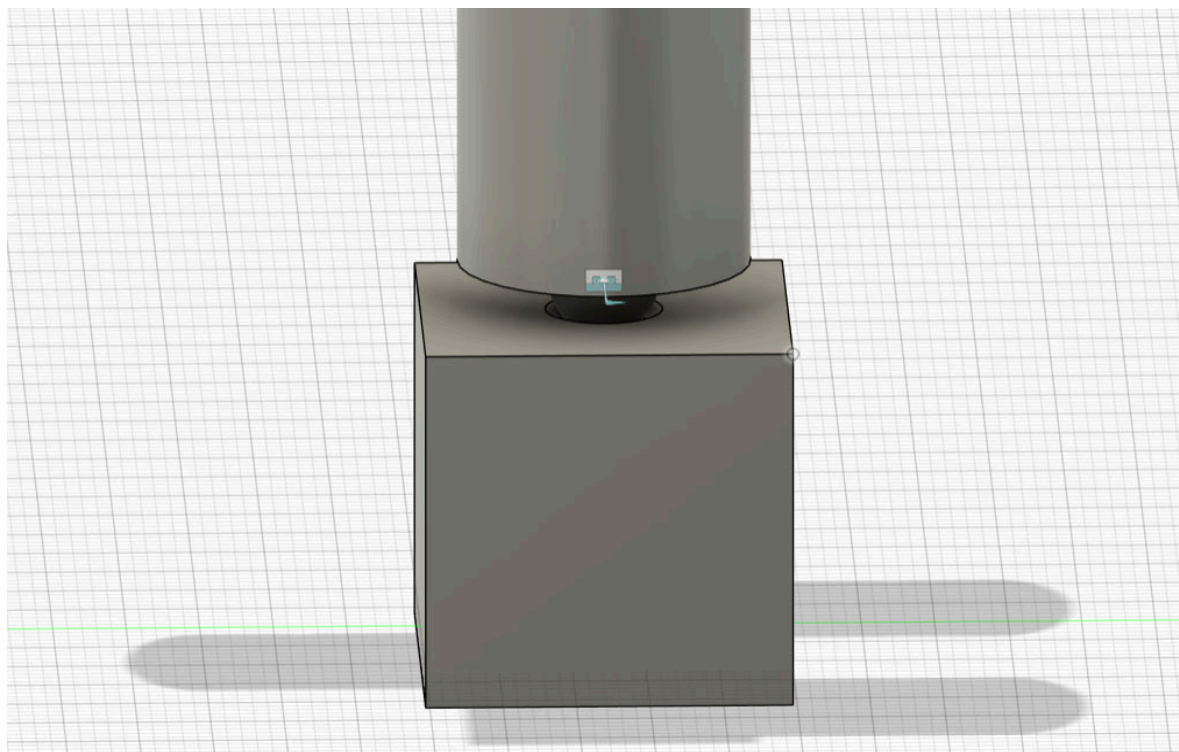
Опорна конструкція для захватного пристрою
